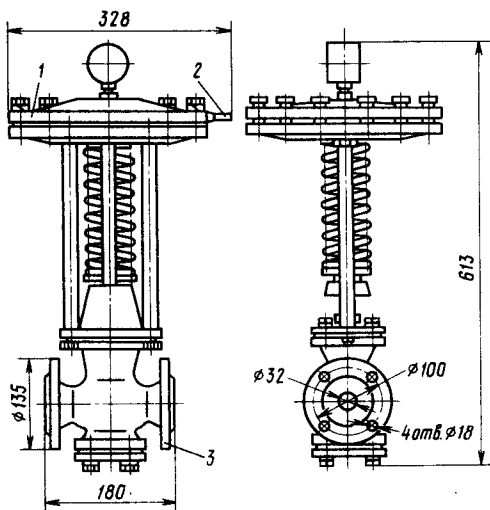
Общий вид и размеры регулятора давления РД-32:
